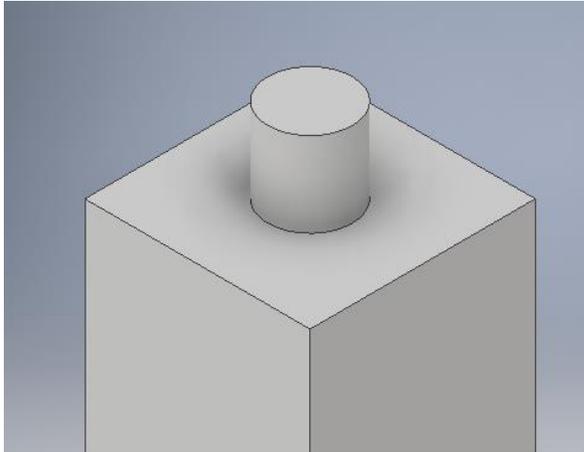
Pieza de ensamble entre base de patas y bobinas.
